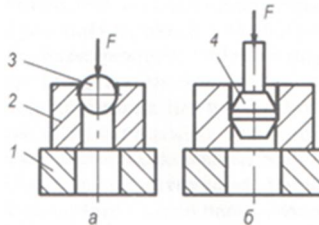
Схема обкочування (а) і розкочування (б) циліндричних поверхонь
